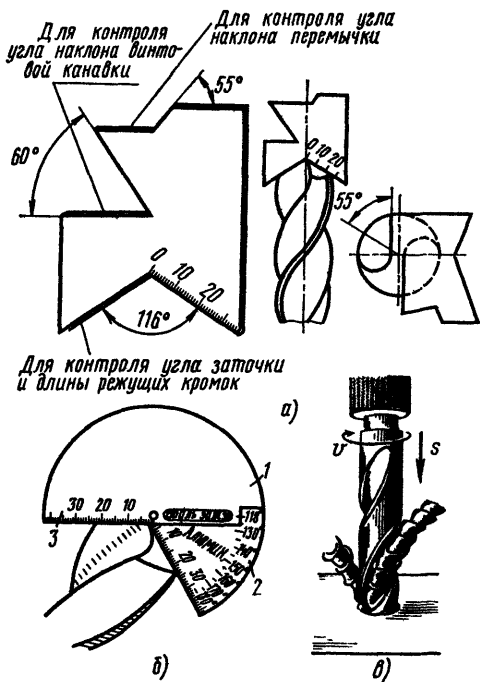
Проверка качества заточки сверла: а — по шаблону, б — универсальным угломером, в — пробным сверлением
